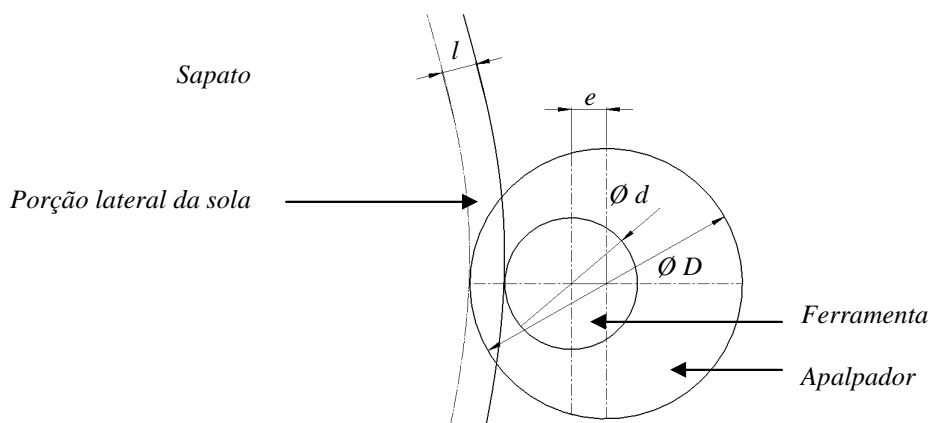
Desenho esquemático das dimensões do apalpador.
